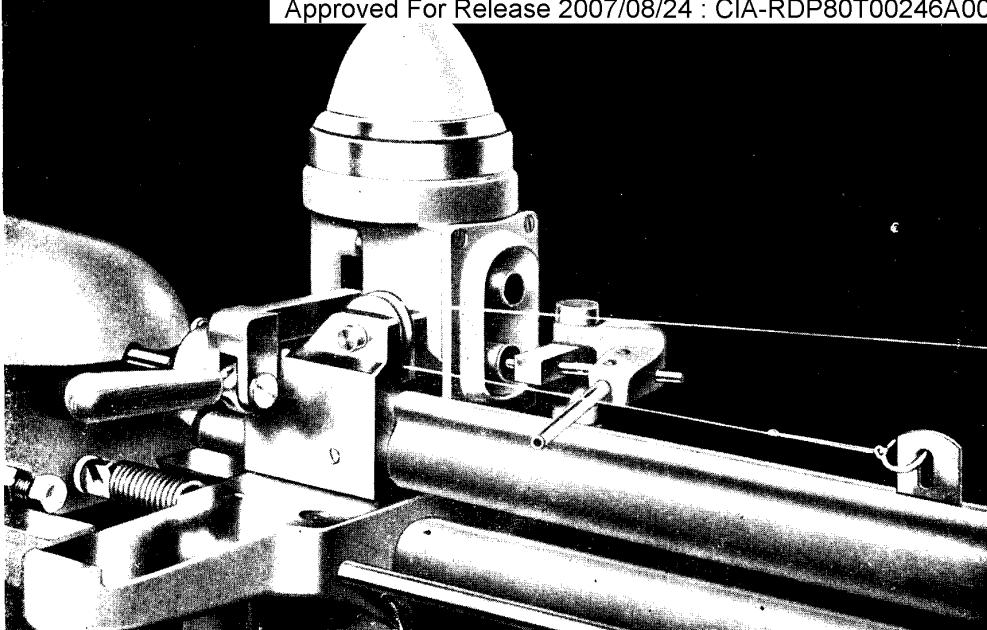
ZWEIKNOFFSCHALTER DER FERNSTEUERUNG UND DIE SIGNALLAMPE DES DREHAUTOMATEN BP-U12
